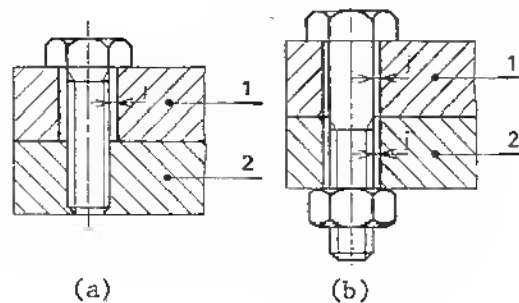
Assemblage de deux plaques par (a) vis et (b) boulon. j est le jeu radial.
